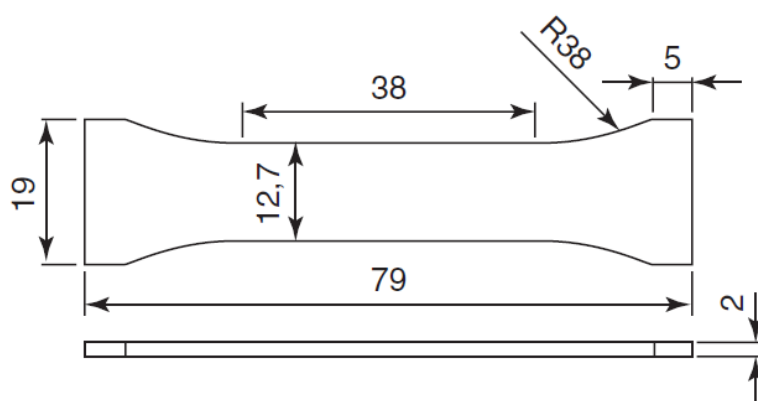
Provete plano para ensaio de compressão (ASTM D 695) (dimensões em mm) [20]
